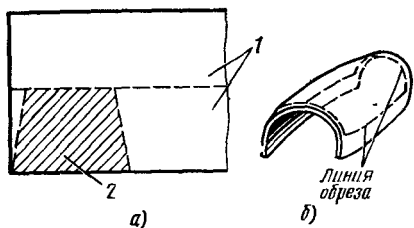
Схема изготовления детали оболочки самолета двойной кривизны: а — раскрой листа на полосы 1 и полос на заготовки 2; б — заготовка после обтягивания на ОП-3
